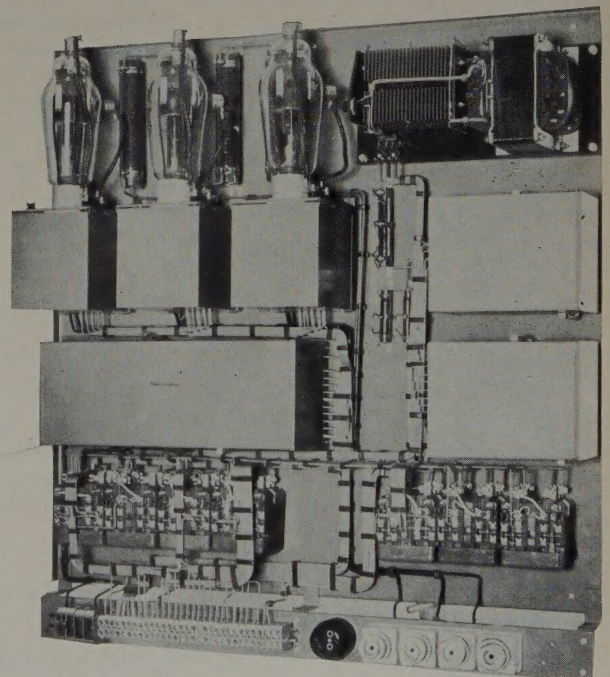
Einbauchassis für den Vorschubantrieb einer Fräsmaschine
